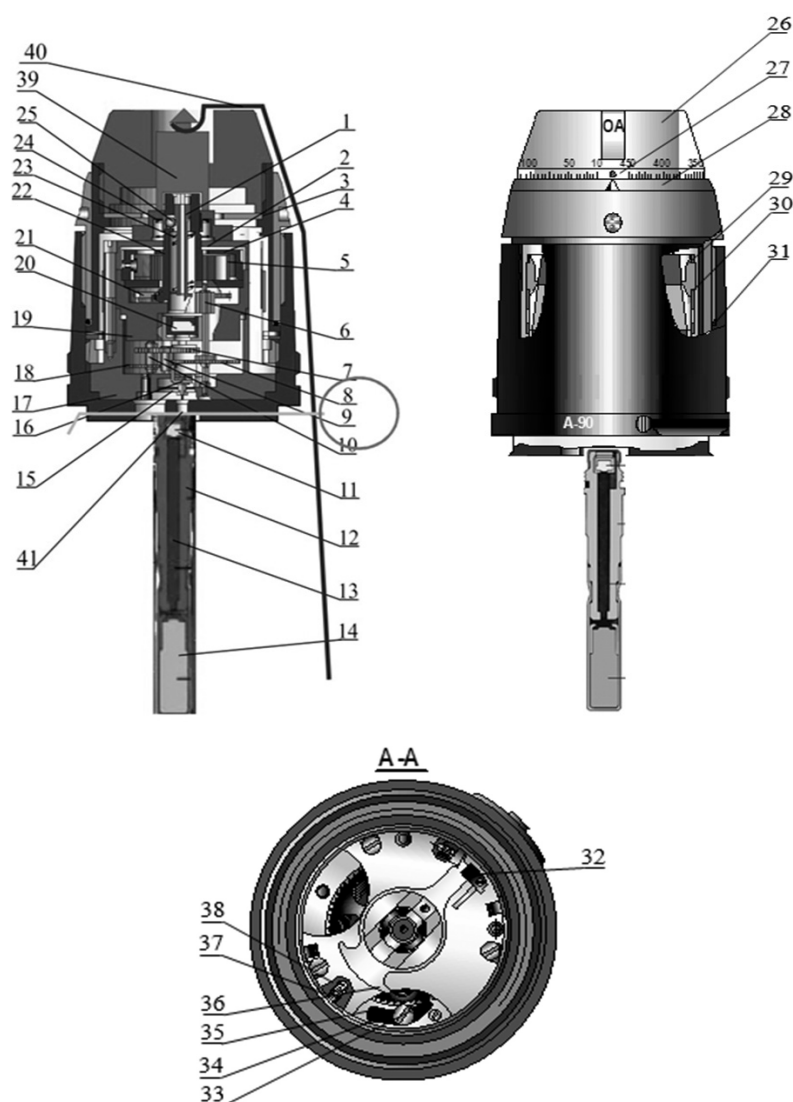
Взрыватель дистанционного подрыва ручных гранат: двигатель: 5 — заводная пружина, 4 — барабан, 22 — центральная ось, 35 — защелка, 34 — ось защелки, 33 — пружина; колесная передача: 21 — центральное колесо, 7, 8 — зубчатые колеса, 6, 9, 10 — трибы; регулятор хода: 18 — ходовое колесо, 16 — баланс с грузиками, 15 — пята; установочное устройство: 26 — головная втулка, 27 — установочная втулка, 28 — соединительное кольцо, 3 — установочная планка, 36 — стрела, 31 — гофрированное пружинное кольцо; фиксирующее устройство: 29 — ножи, 30 — фиксирующее кольца, 37 — стопоры, 38 — пружины; исполнительное устройство: 1 — ударник, 2, 17, 19 — планки, 20 — капсуль-воспламенитель, 23 — пружина, 24 — пружина, 25 — шарики, 32 — предохранительная скоба, 39 — упор, 40 — спусковой рычаг, 41 — предохранительная чека; запал: 11 — капсуль-воспламенитель, 12 — втулка замедлителя, 13 — замедлитель, 14 — капсуль-детонатор
